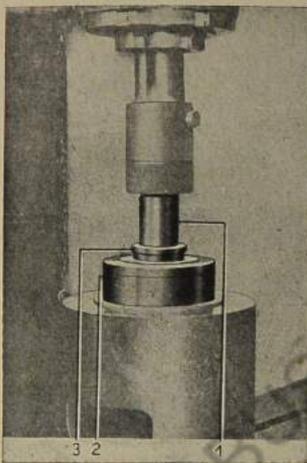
Zwischenradwelle in Laufring für Zylinderrollenlager einpressen
